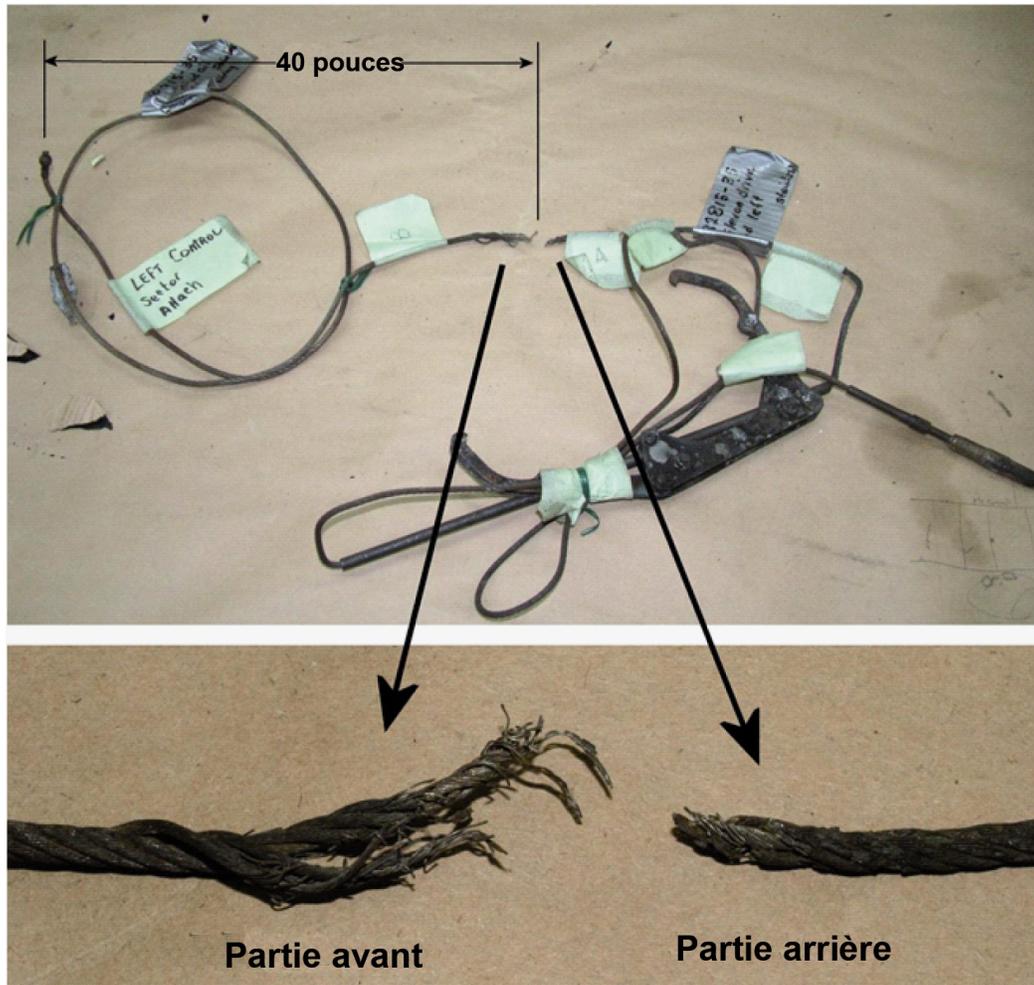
Assemblage du câble de commande d'aileron avant gauche sectionné, tel que reçu par le laboratoire du BST.
